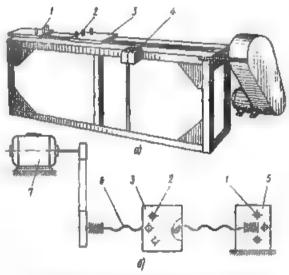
Станок для растяжки круговых заготовок а – общий вид, 6 – кинематическая скема
